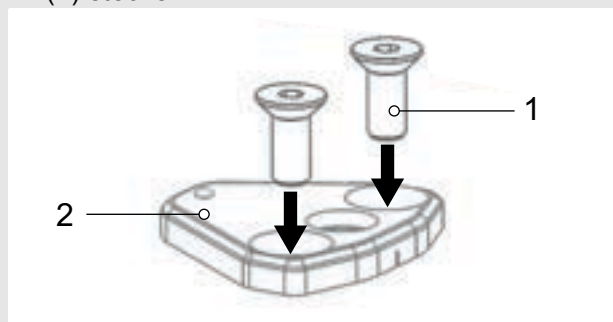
Senkkopfschrauben in Basisplatte stecken
